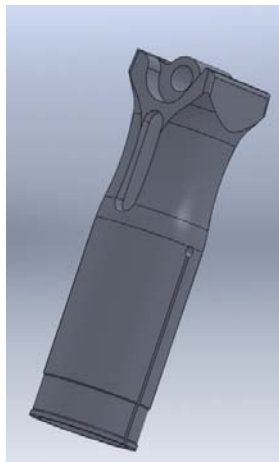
Imagen isométrica de Parte Inferior Tubular.
